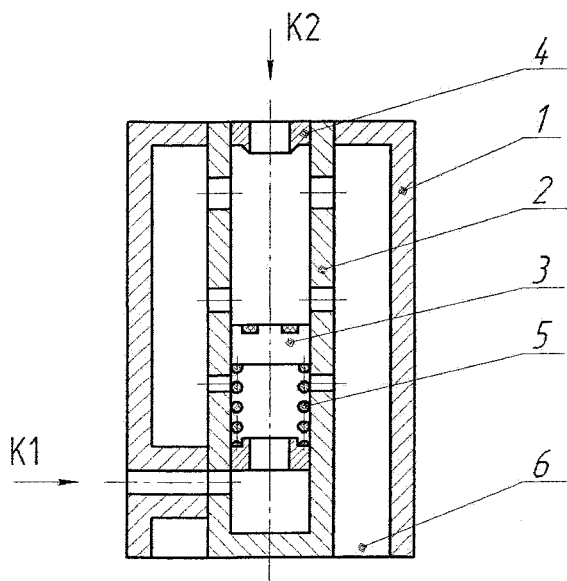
Двухкомпонентная многорежимная форсунка: 1 – внешний корпус; 2 – внутренний корпус; 3 – поршень; 4 – седло; 5 – пружина; 6 – сопло
